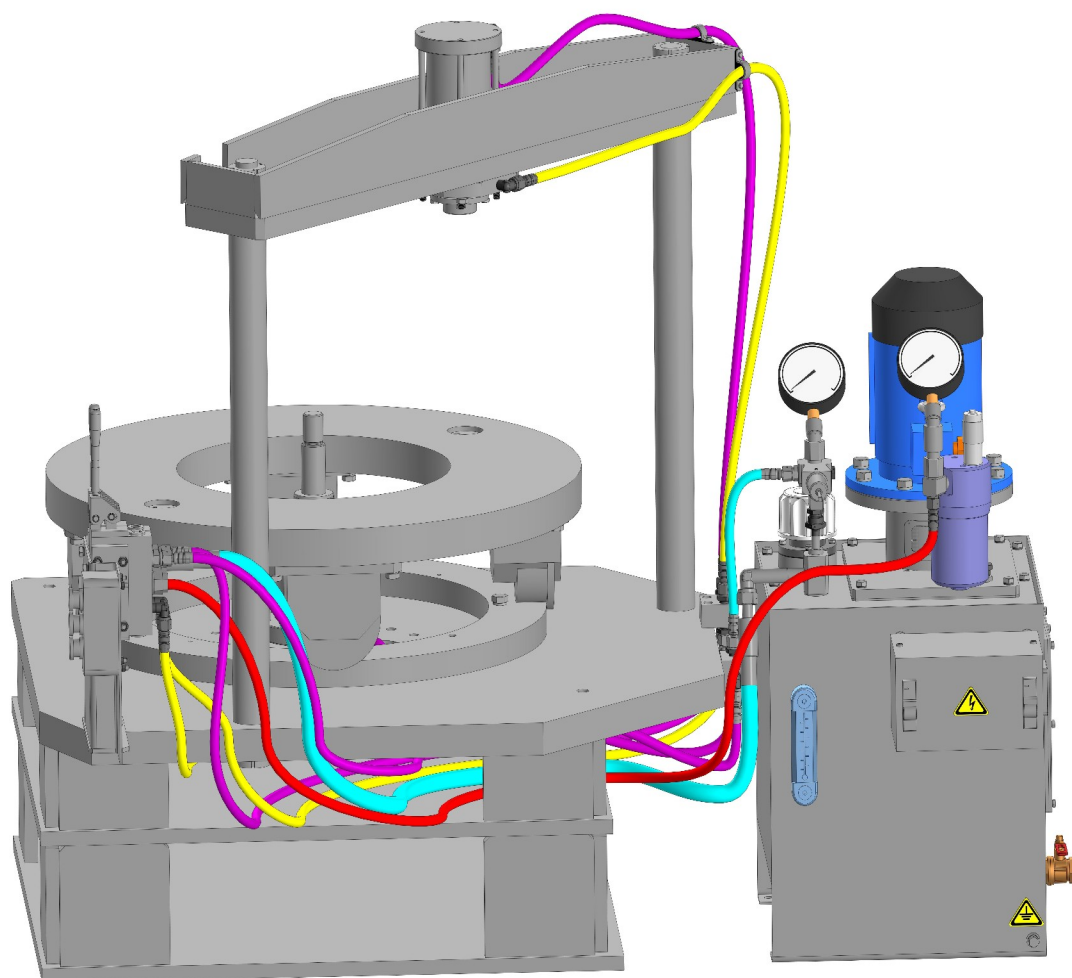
3D-модель устройства для запрессовки составного зубчатого колеса
